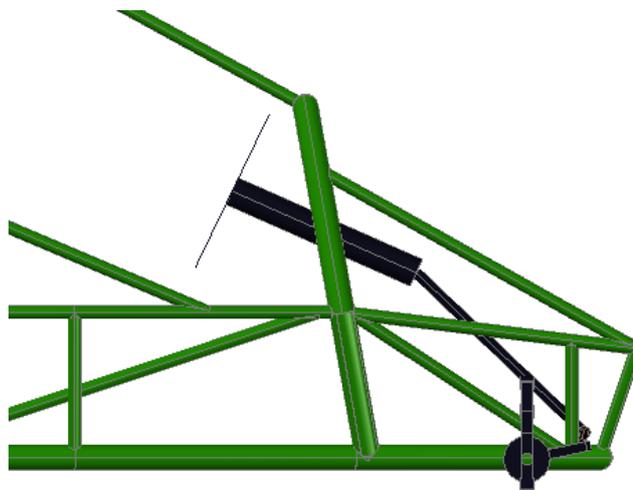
Vista lateral configuración Volante, barra de dirección⁶¹.
